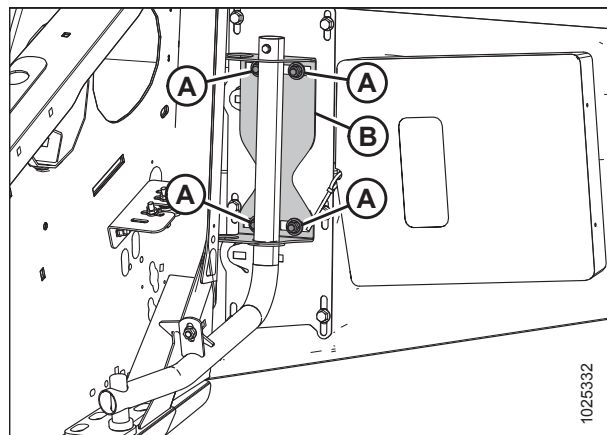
Tubo de soporte de la parte lateral izquierda
